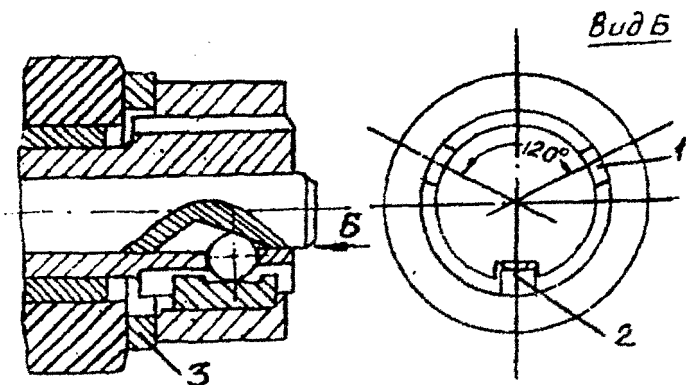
Установочно-разжимная оправка с двумя неподвижными и одним подвижным кулачками
